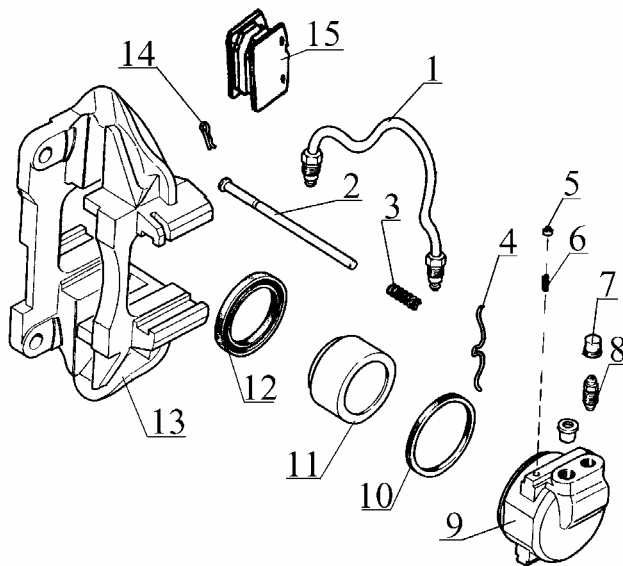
Детали суппорта переднего тормоза 2101-3501010-02/11-02:
